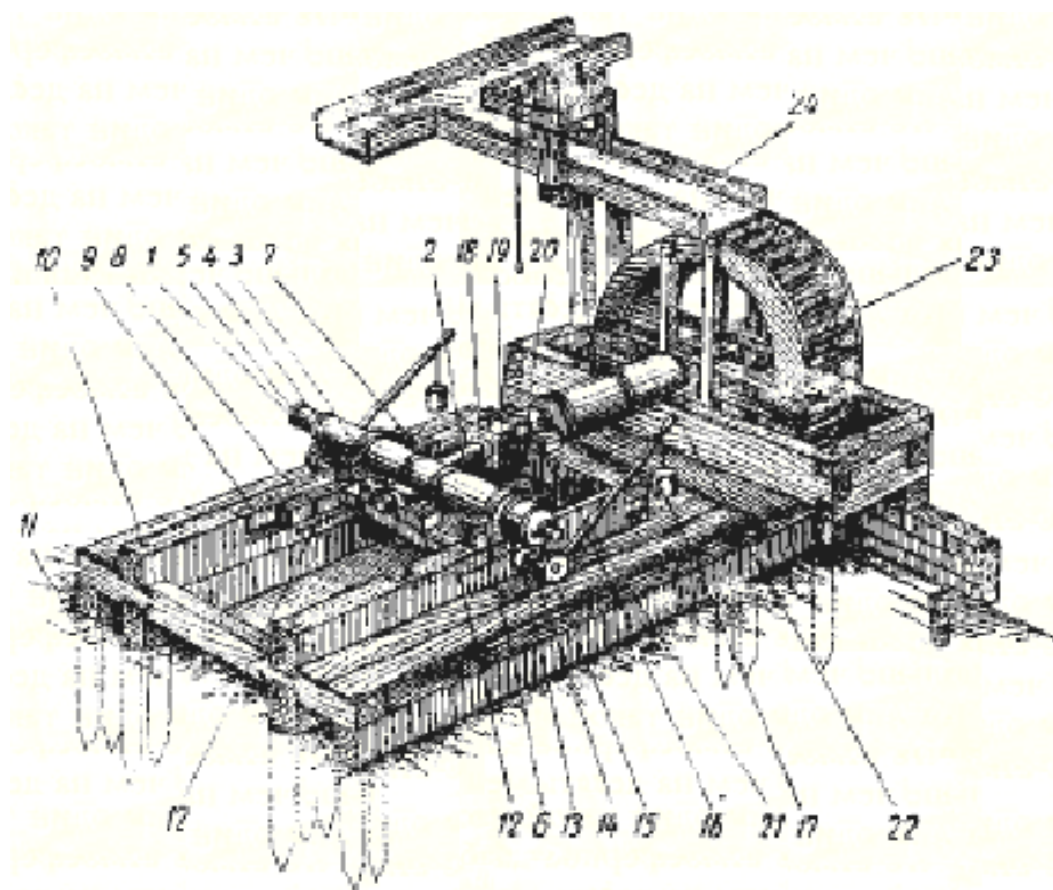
Станок для обточки цапф стволов орудий А. К. Нартова
